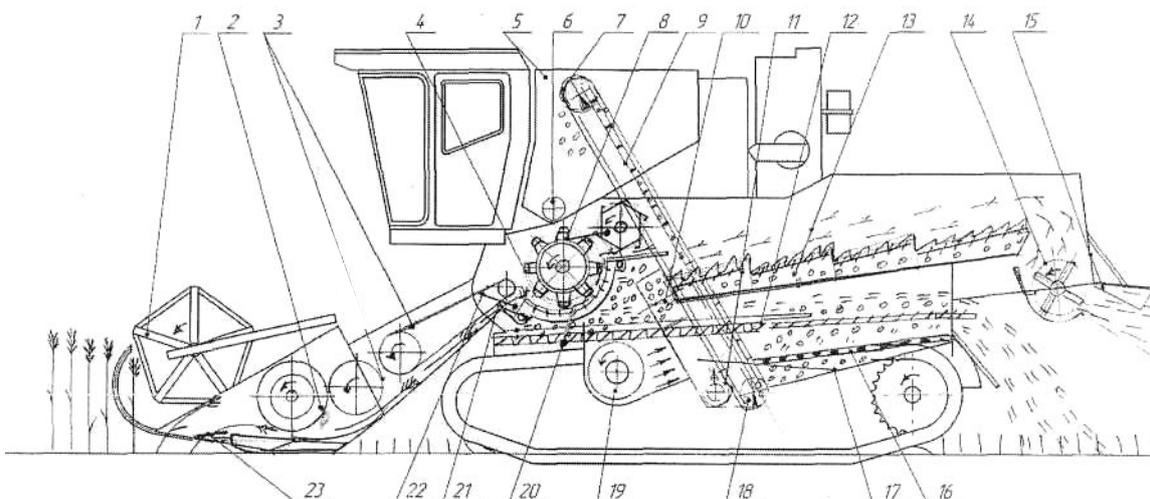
Схема технологического процесса работы комбайна КЗС-3Г при уборке урожая прямым способом: 1-мотовило; 2-шнек жатки; 3-наклонный транспортер; 4-молотильный эрабан; 5-бункер; 6-выгрузный шнек бункера; 7-распределительный шнек зункера; 8-отбойный битер; 9-зерновой элеватор; 10-домолачивающее /стройство; 11-колосовой элеватор; 12-верхнее решето; 13-соломотряс; 14-азмельчитель; 15-разбрасыватель; 16-нижнее решето; 17-колосовой шнек; 18- зерновой шнек; 19- вентилятор; 20-ступенчатая стрясная доска; 21- подбарабанье; 22-камнеуловитель; 23-режущий аппарат
